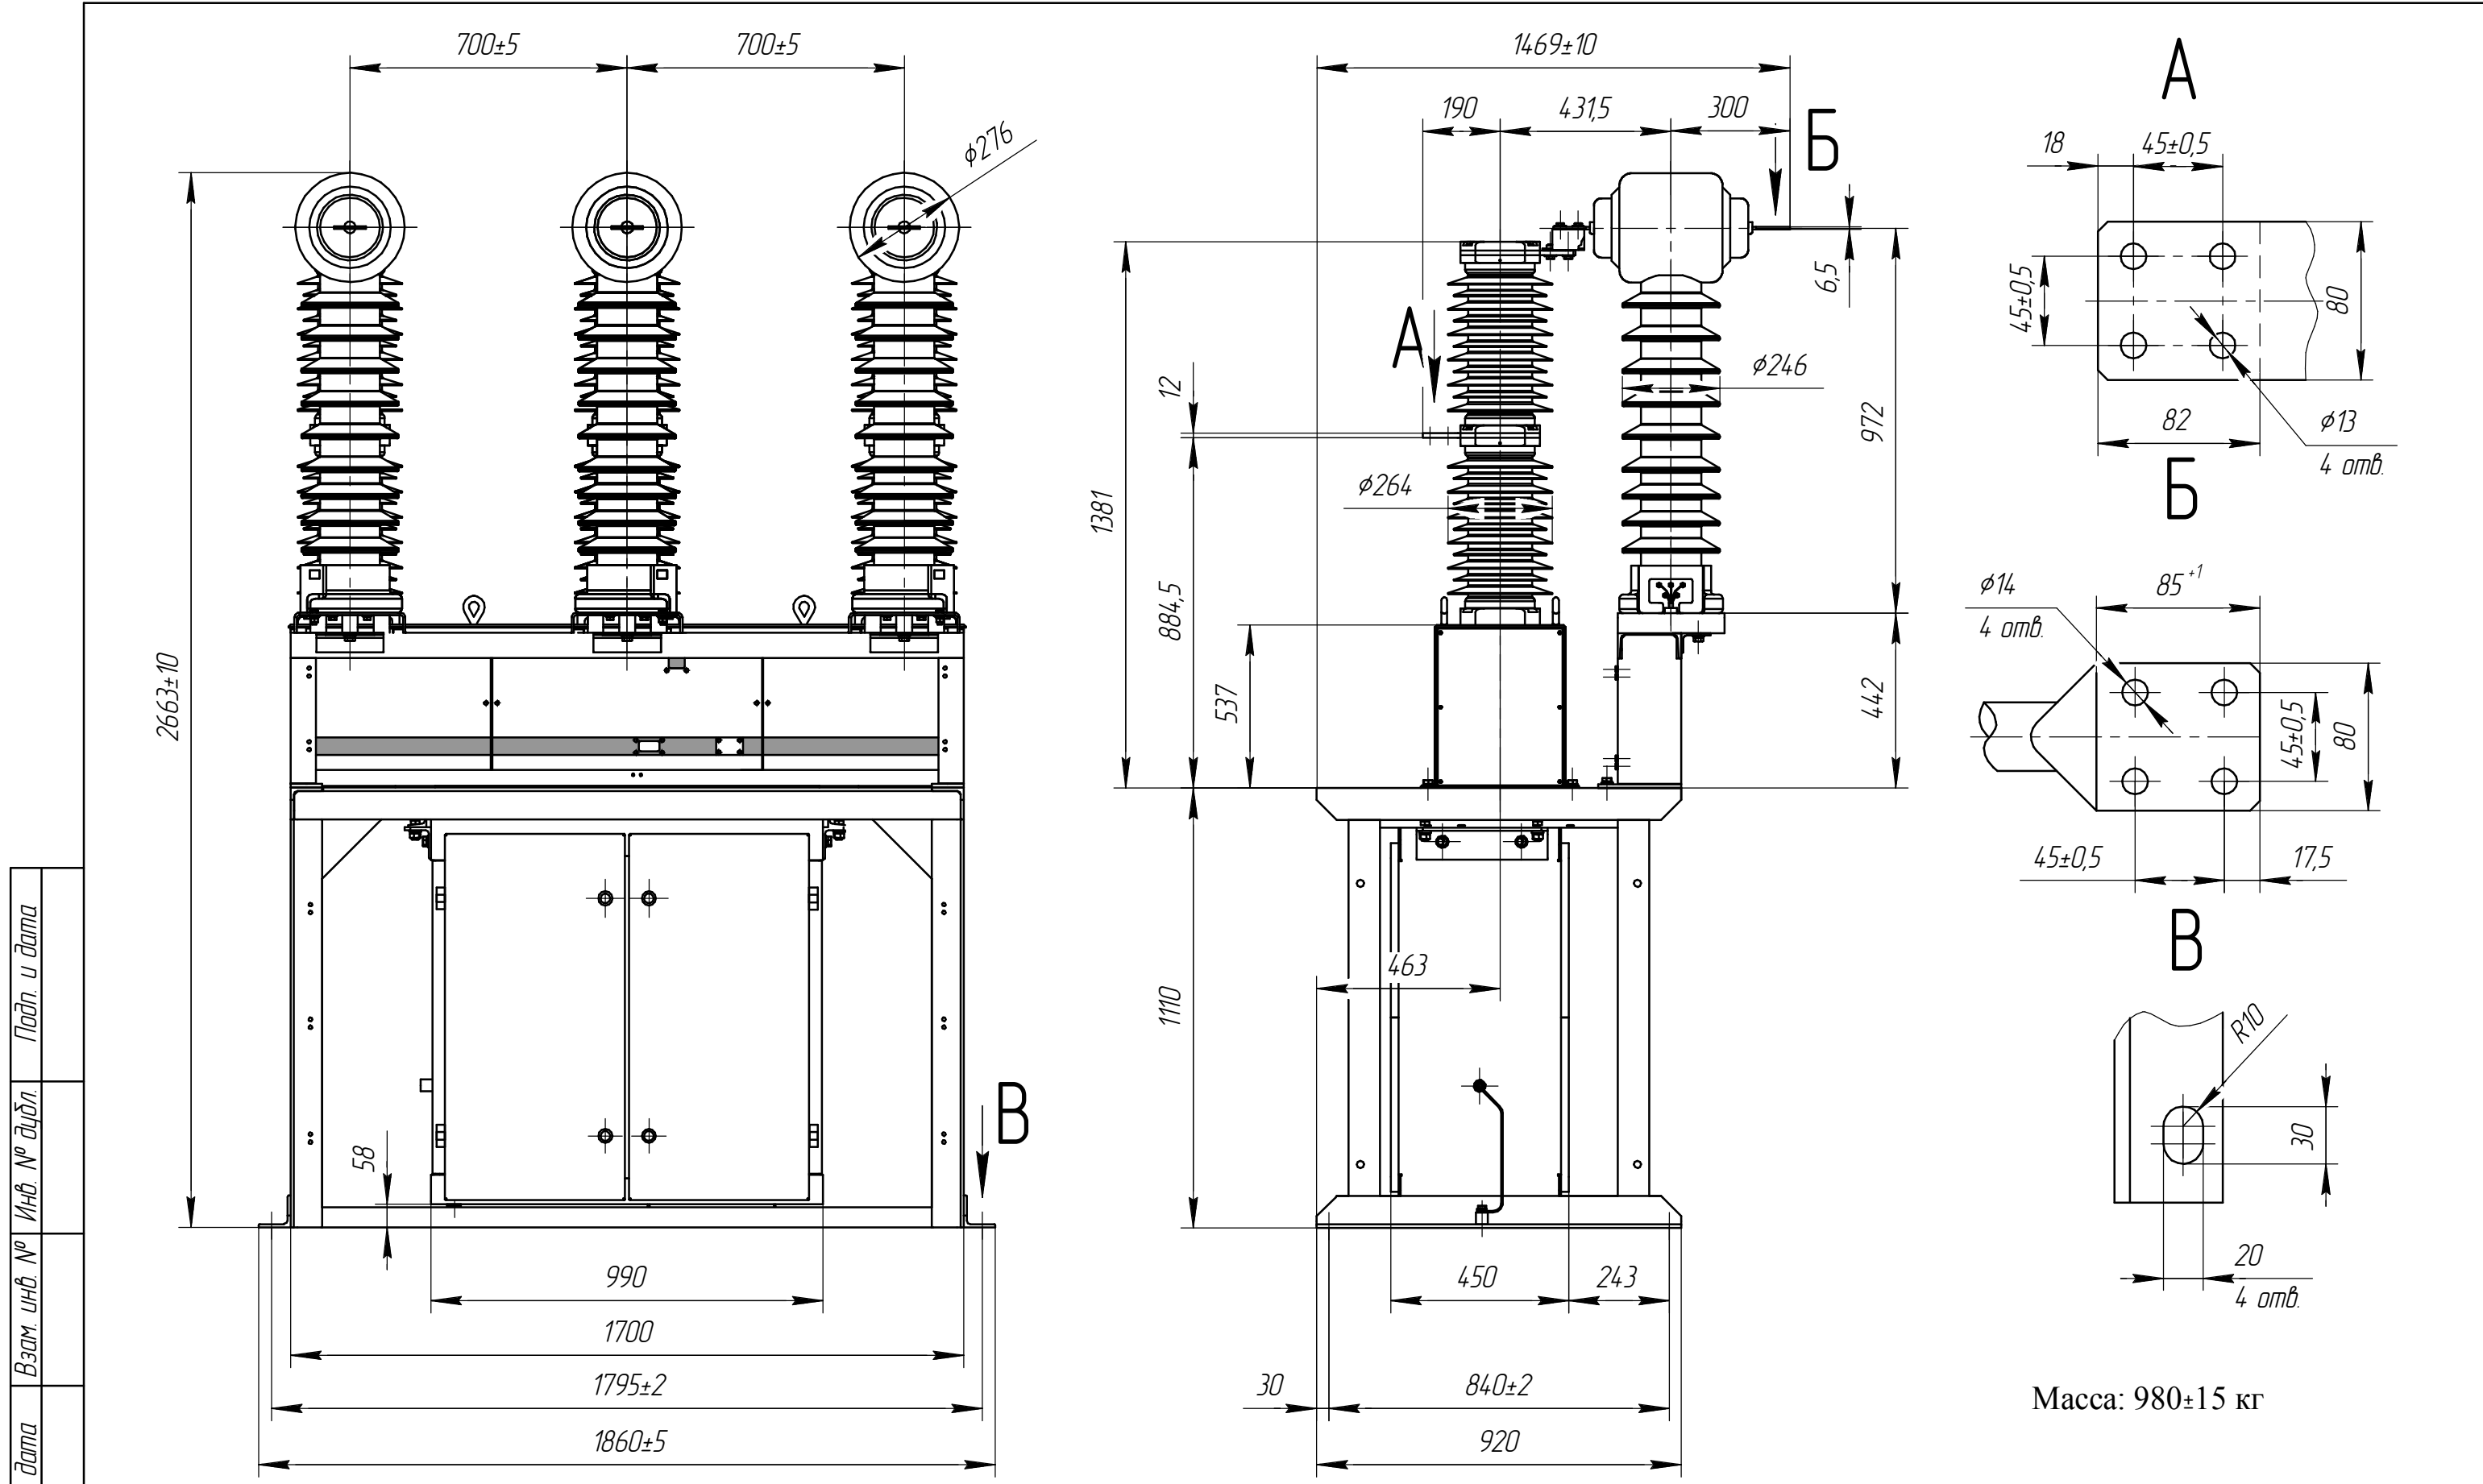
Габаритные, установочные и присоединительные размеры выключателя типоразмера ВР35НТ-35-25/1600-0/3 УХЛ1 с тремя встроенными трансформаторами тока ТОЛ-35 III-IV-2; 4; 6; 8 УХЛ1 со стороны верхних контактов
